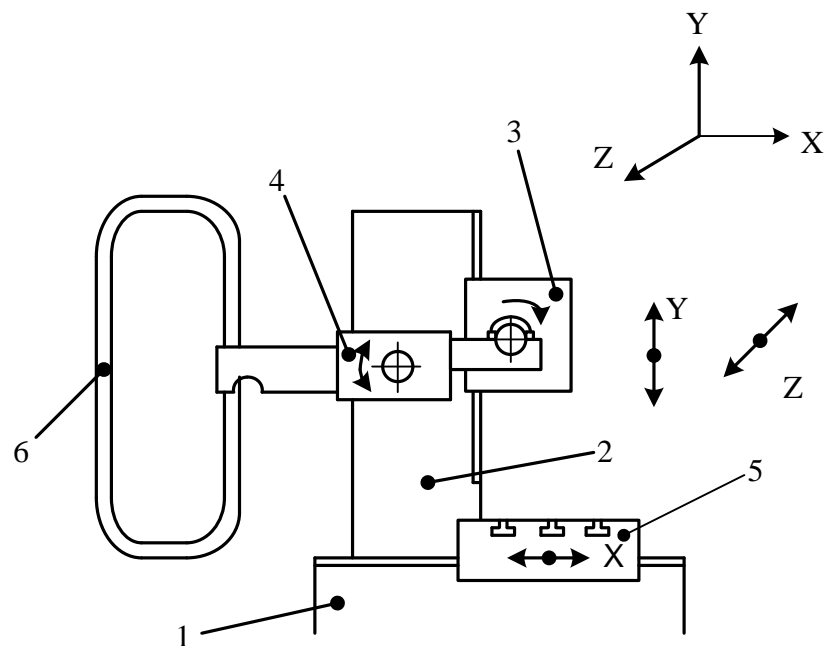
Горизонтальна компоновка багатоопераційного верстату:
